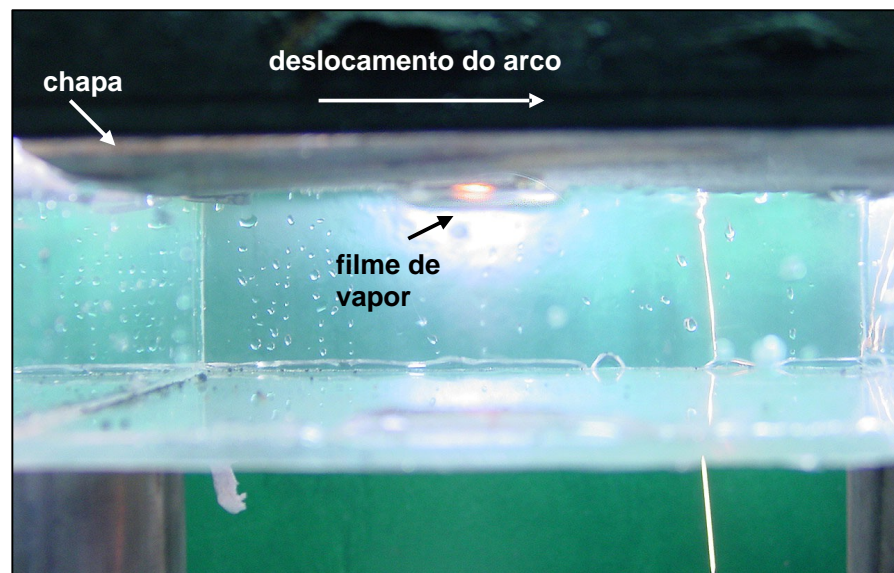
Deslocamento de filme de vapor junto à superfície da chapa em contato com a água.
